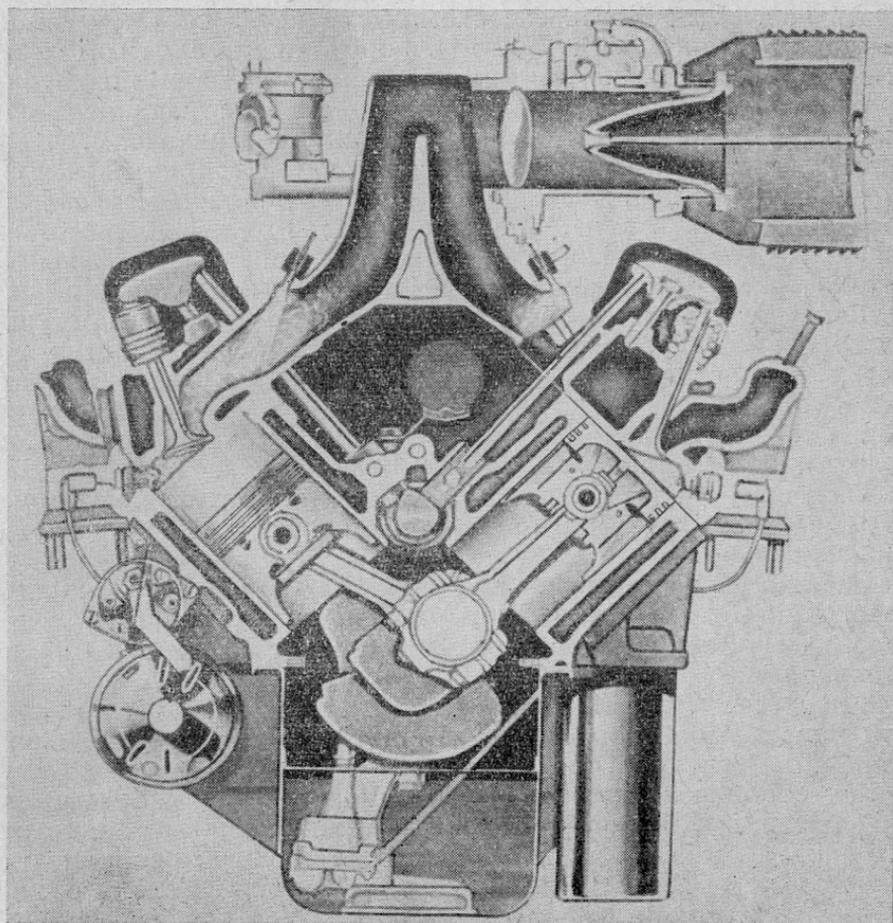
Поперечный разрез V-образного 8-цилиндрового двигателя Chevrolet-Corvette 1957 г. с впрыском бензина
